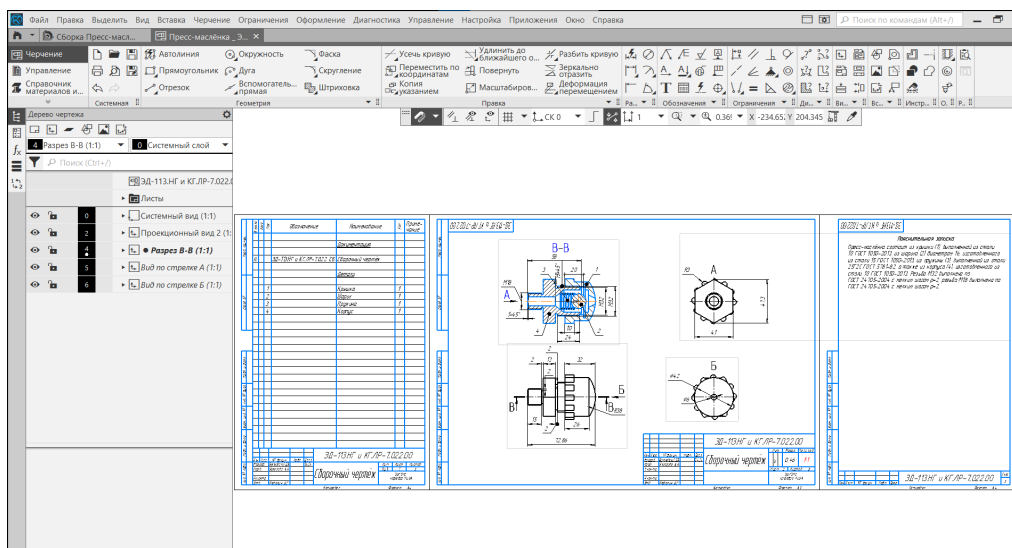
Пример оформления сборочного чертежа пресс-масленки в «КОМПАС-3D»
